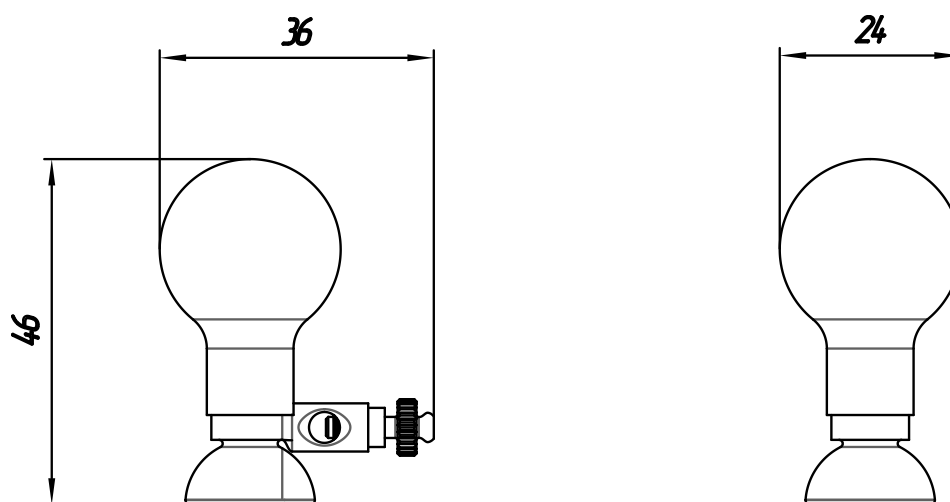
Габаритные размеры «Грудной детский ЭХС-06д (6 шт)»
